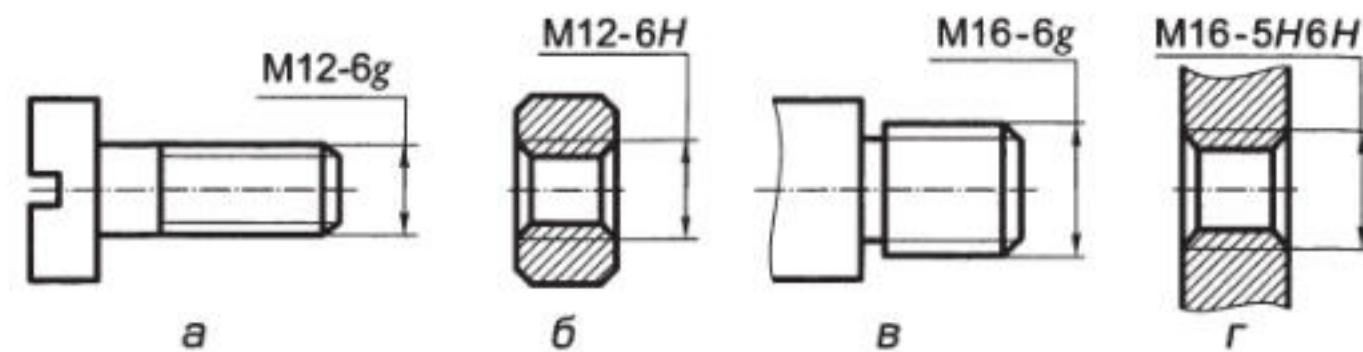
Условные обозначения метрических цилиндрических резьб:
